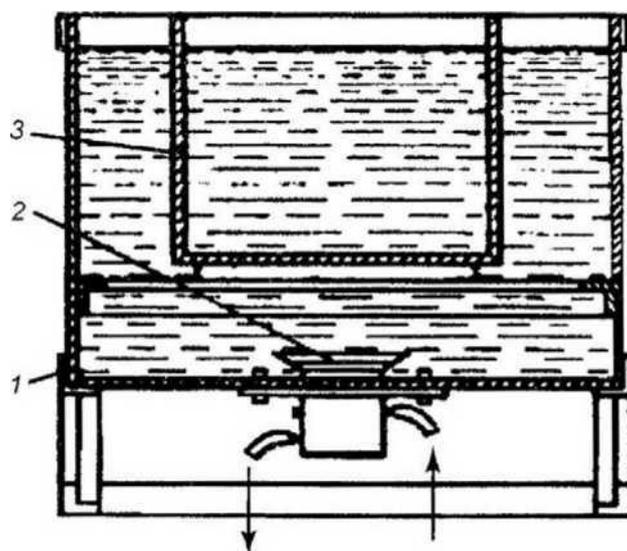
Схема установки для очистки деталей косточковой крошкой:
